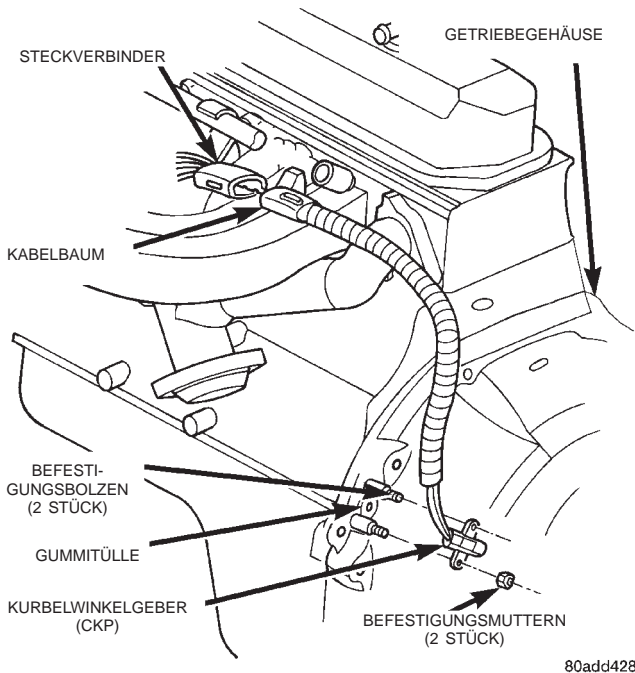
Kurbelwinkelgeber (CKP)—2.5L-Vierzylindermotor—Automatikgetriebe
